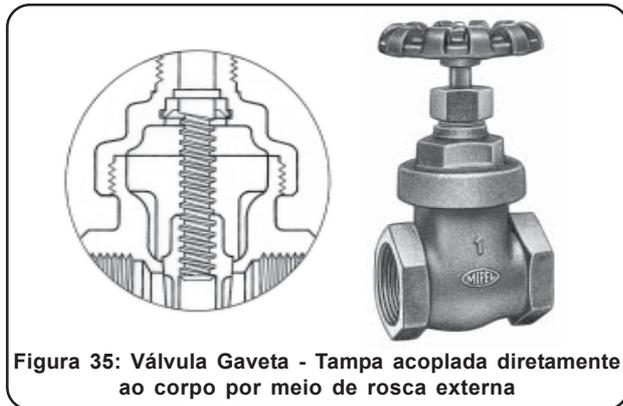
Válvula Gaveta - Tampa acoplada diretamente ao corpo por meio de rosca externa
